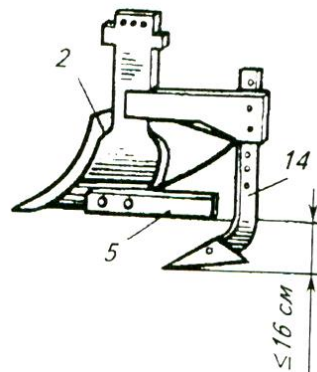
Схема корпуса с почвоуглубителем
